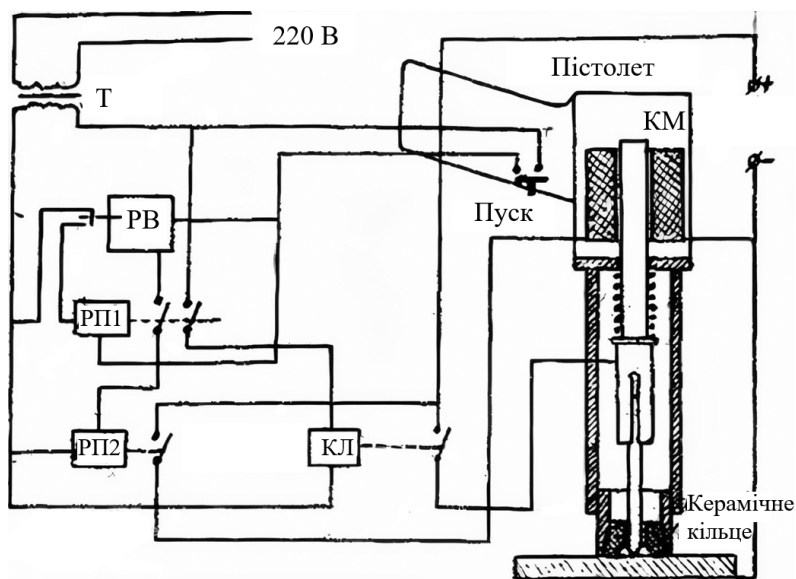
Принципова схема установки для дугового приварювання шпильок
